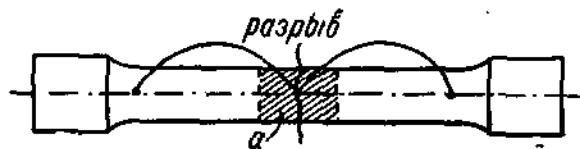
Кривая удлинений образца, сваренного металлической дугой.
